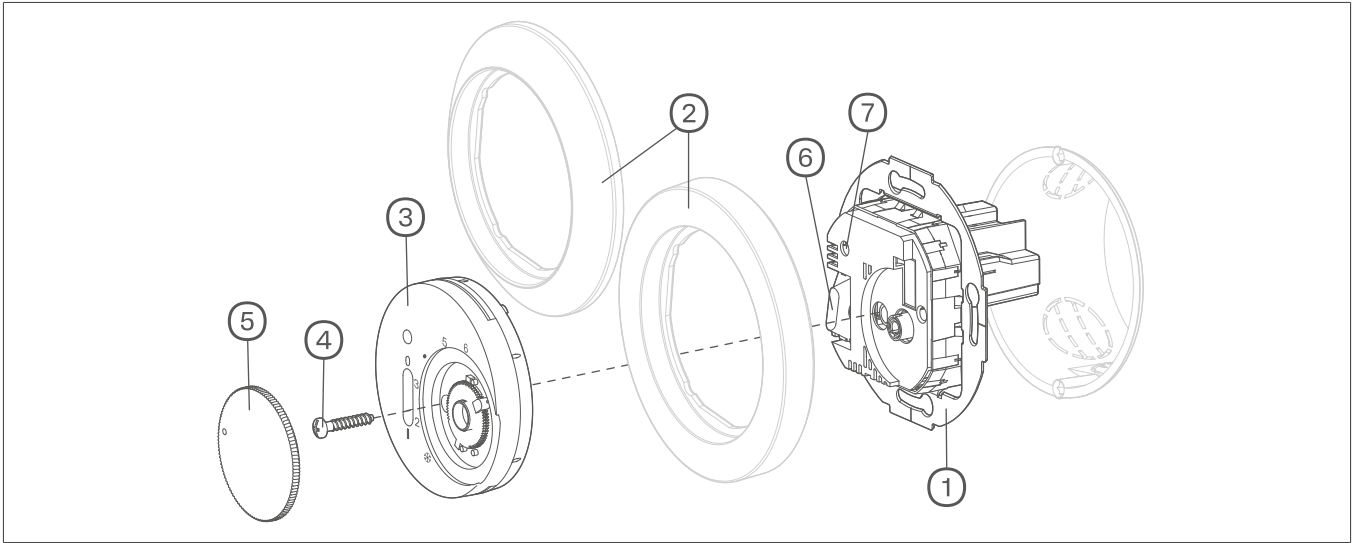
Disegno e struttura del dispositivo WLN5030xx
